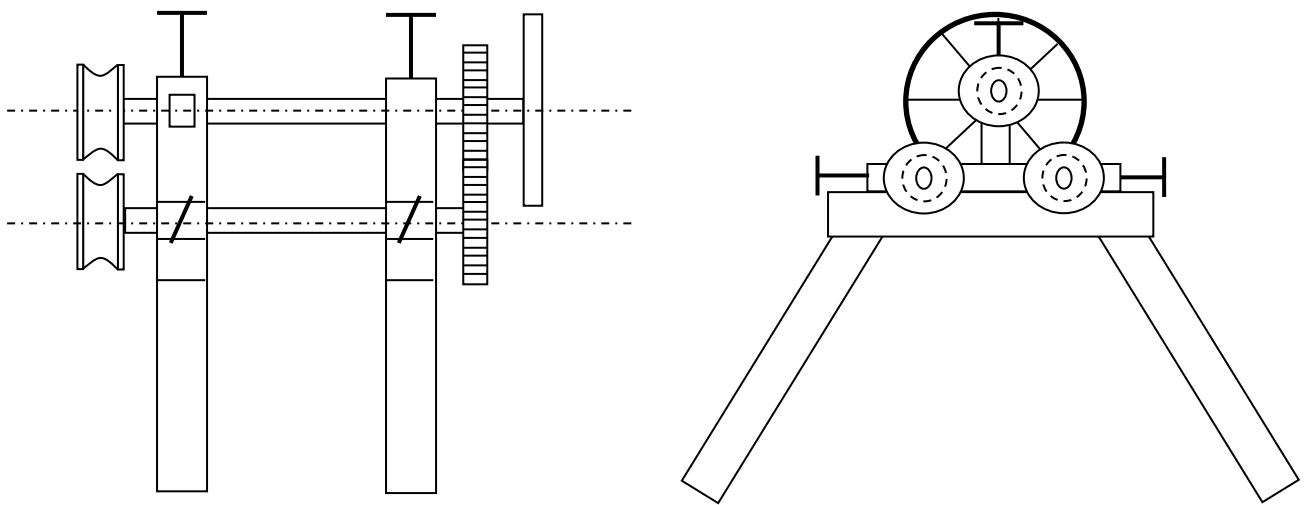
Roladora con sistema de transmisión por engranajes.
